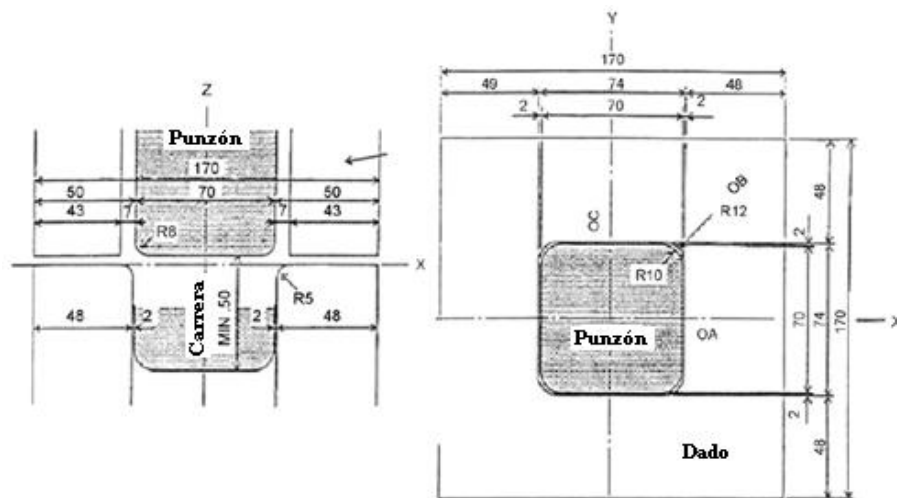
Dimensiones de las herramientas para el embutido cuadrado (Makinouchi [48])
